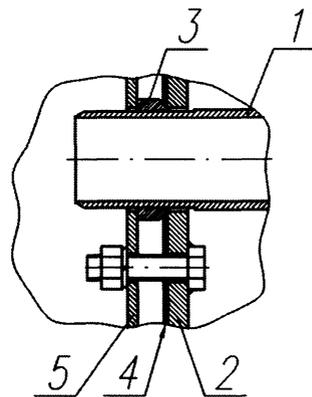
Схема компенсатора для конвективного рекуператора: 1 - труба теплообменника; 2 - трубная доска; 3 - втулка; 4 - прокладка; 5 - прижимная плита
